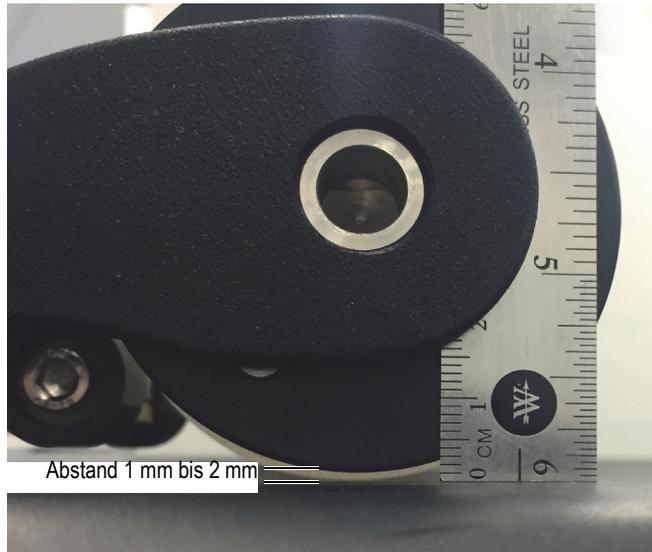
Abstand zwischen Flansch der Akustikrolle und Prüffläche (RollerFORM XL)
